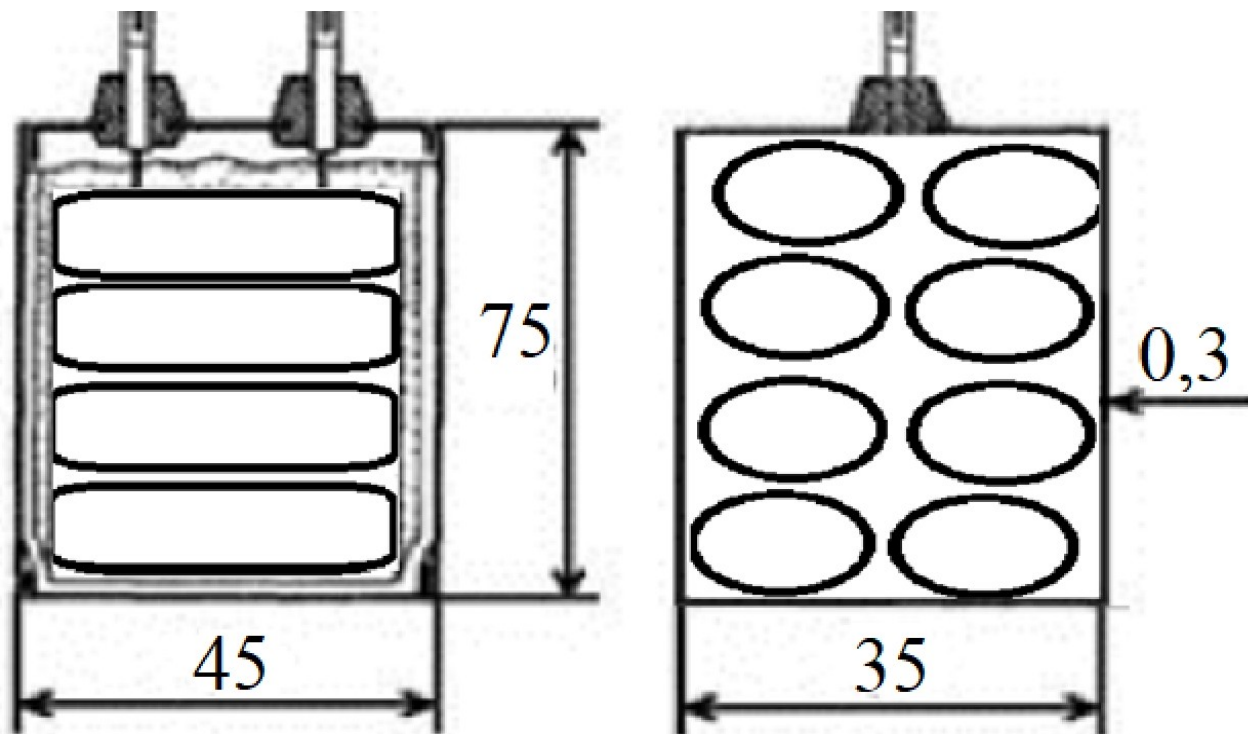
Бумажный конденсатор в корпусе вид спереди и сбоку
